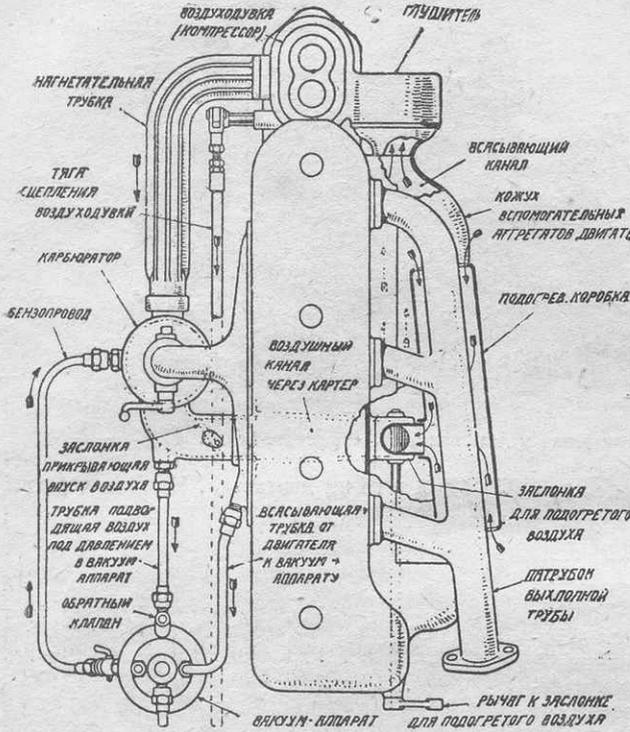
Схема устройства компрессорного двигателя «Мерседес-Бенц».
